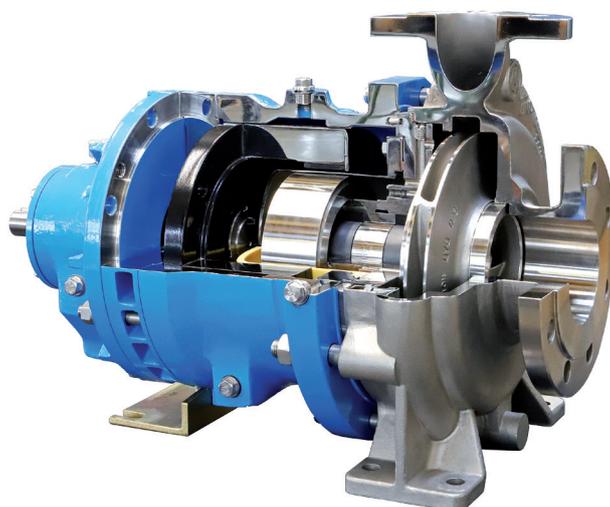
Standard-Hydraulikeinheit – identisch mit der einer mechanisch abgedichteten Pumpe
